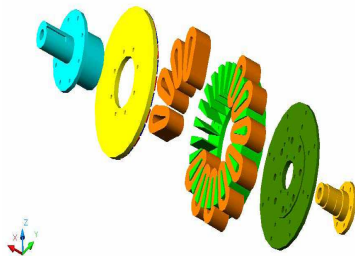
Machine à flux axial 1 stator/1 rotor avec bobinage sur dents [MAR 06]
